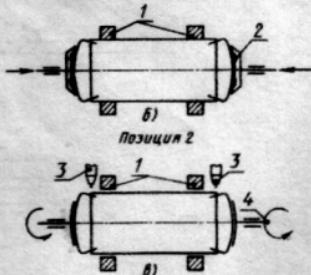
Расположение электрода при сварке кольцевого шва
